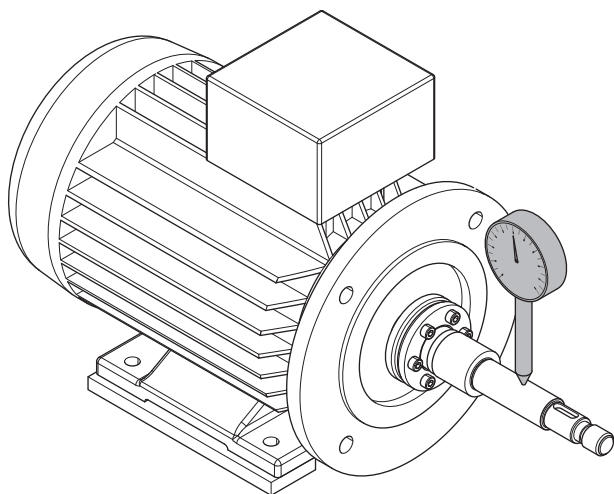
Tolerancia de excentricidad del eje de bomba
